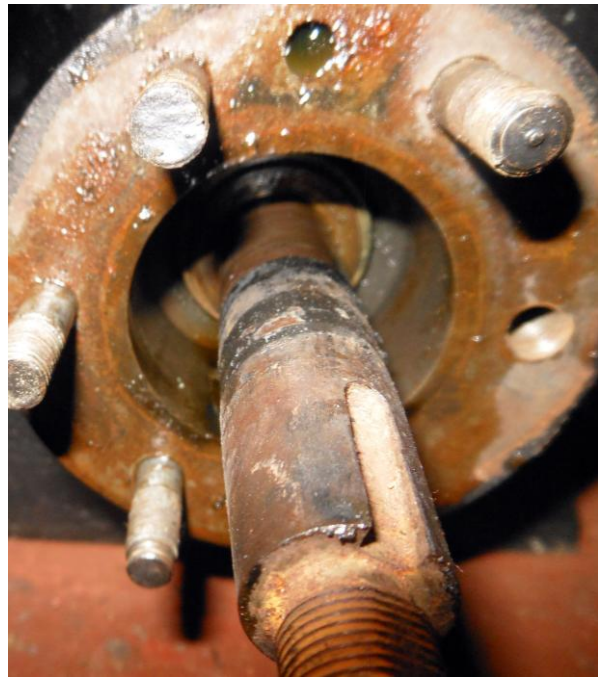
Осмотр поверхности вала в районе установки уплотнительного вращающегося кольца
